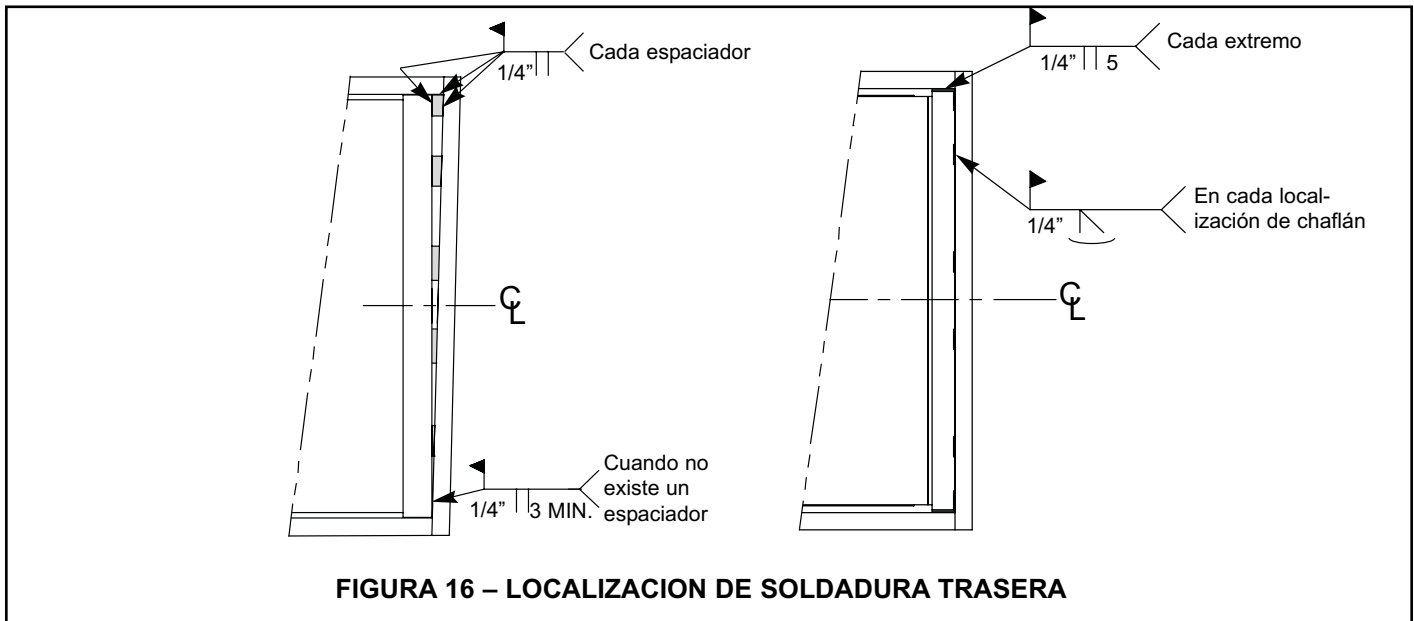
LOCALIZACION DE SOLDADURA TRASERA
